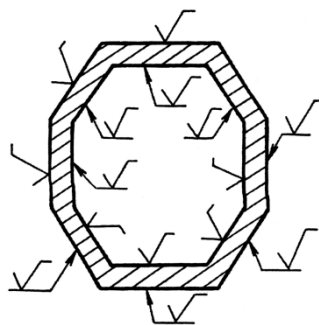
Нанесение знака шероховатости на поверхностях с различным расположением
